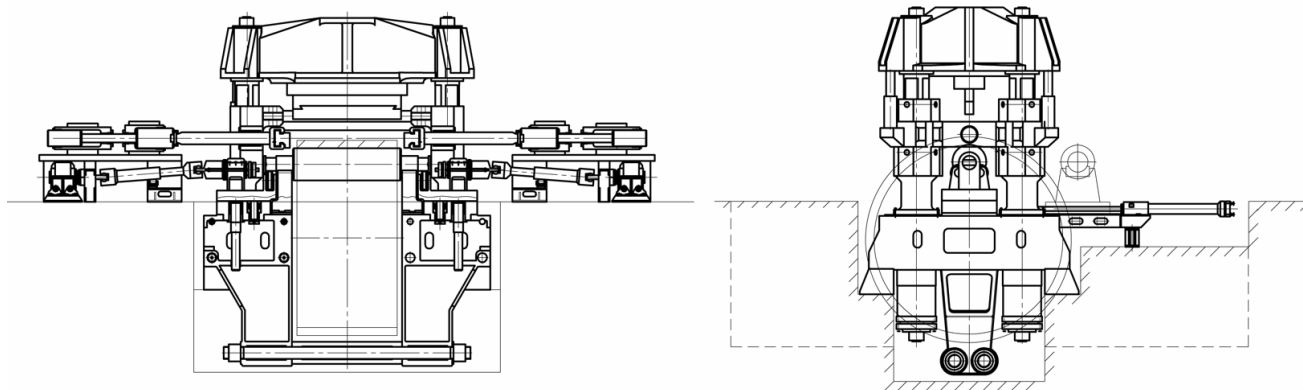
Общий вид ковочного агрегата конструкции ПАО «Уралмашзавод»
